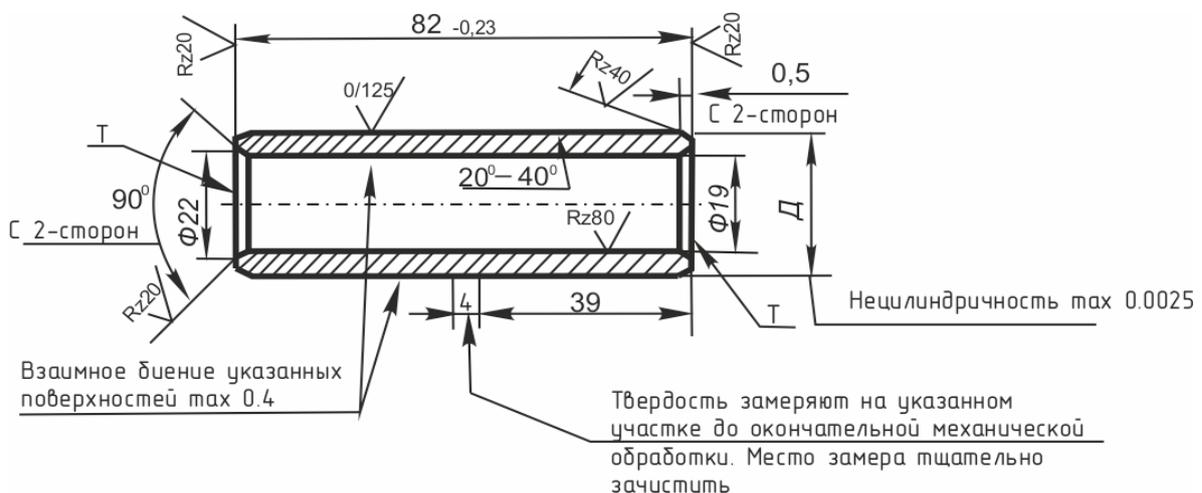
Поршневой палец двигателя ЗИЛ-5 301.
